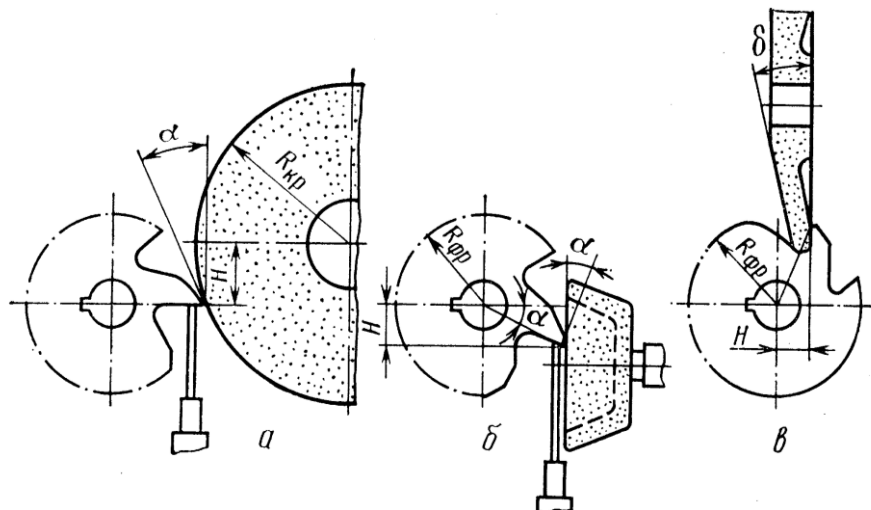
Схема заточування фрез з незатилкованими зуб'ями
